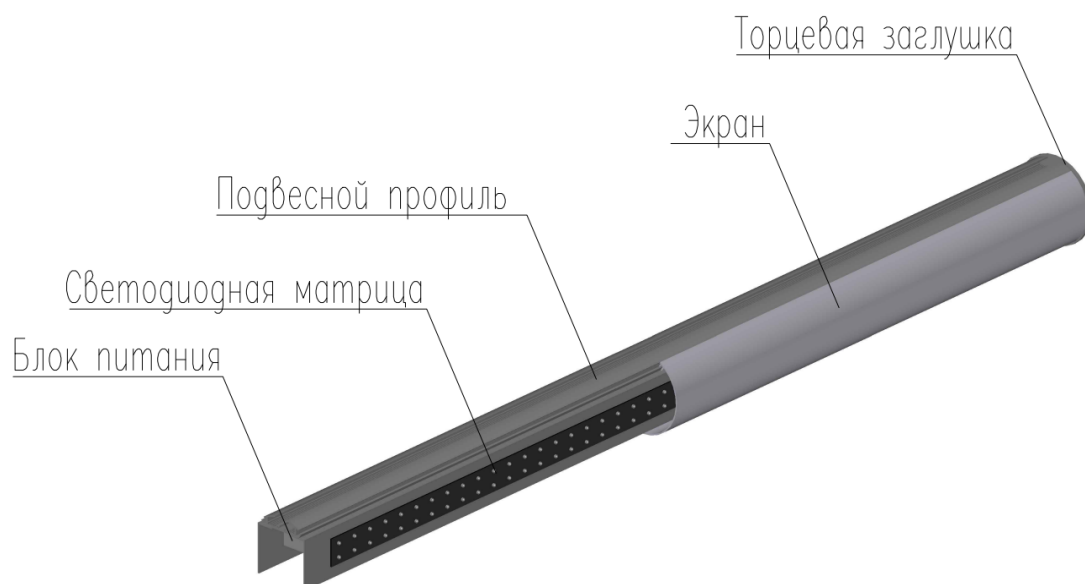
3D-модель макетного образца фитооблучателя
